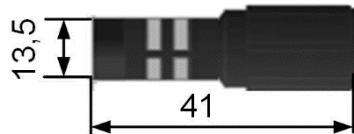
Внешний вид и габаритные размеры укороченного микрофона
